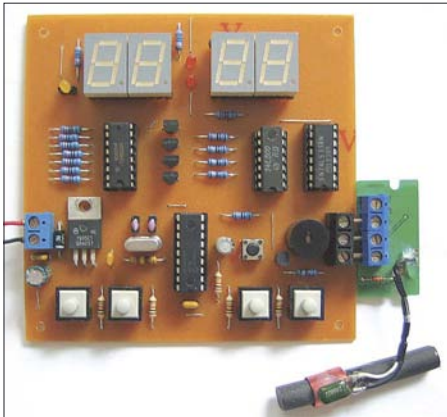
Damit die Baugruppe möglichst flach bleibt und bequem an der Wand befestigt werden kann, wurden alle Bauteile auf einer einzigen Platine untergebracht. Foto: Müller
